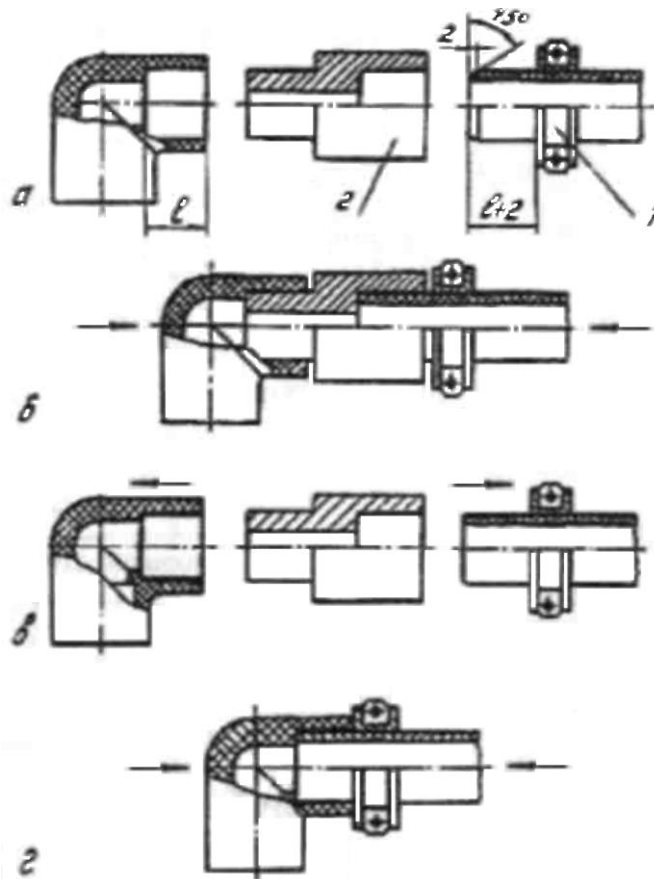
Последовательность процесса контактной сварки в раструб труб и соединительных деталей из ПВД: *а* – центровка, закрепление в зажимах сварочного устройства концов свариваемых труб и деталей и установка ограничительного хомута *1*; *б* – установка дорна нагретого инструмента *2* в раструбе и гладкого конца трубы в гильзе; *в* – нагрев (оплавление) свариваемых концов, одновременно снятие их с дорна и гильзы; *г* – соединение концов с выдержкой до затвердевания сплавленного материала
